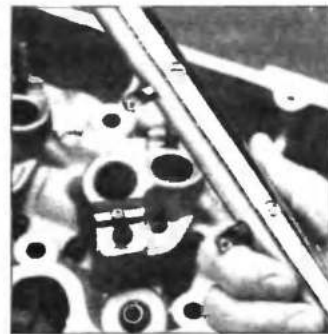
Борштанга с числом резцов, равным количеству опор вала, имеющая два или более подшипника
